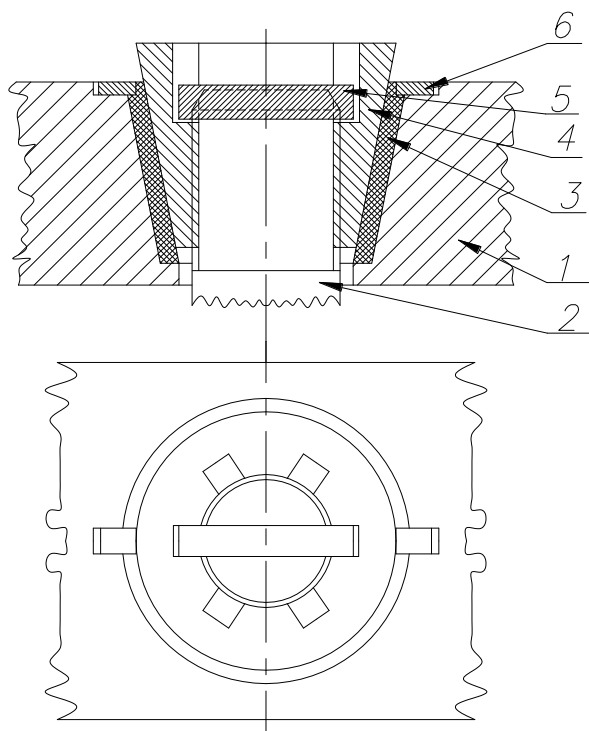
Конструктивна схема шворневого вузла з конусною гайкою:
